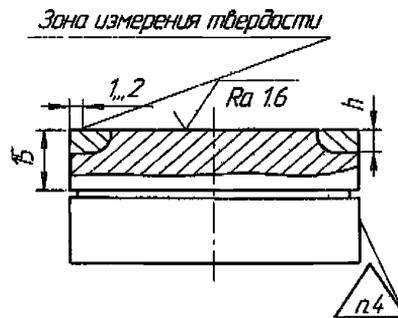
Образец для замера твердости деталей с плоским уплотнением
